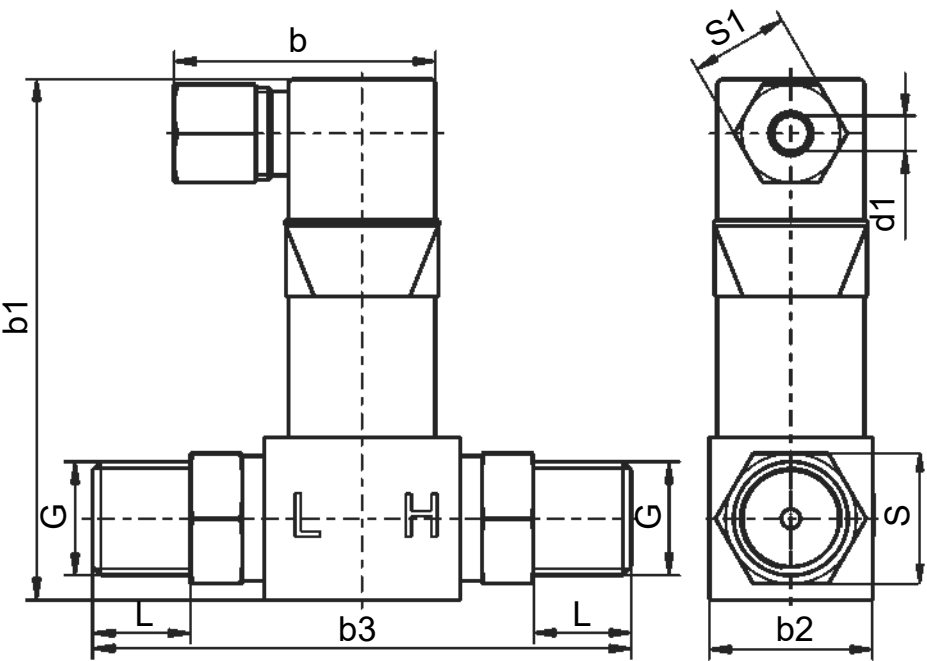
Габаритные и присоединительные размеры датчика давления измерительного РПД-Д.
